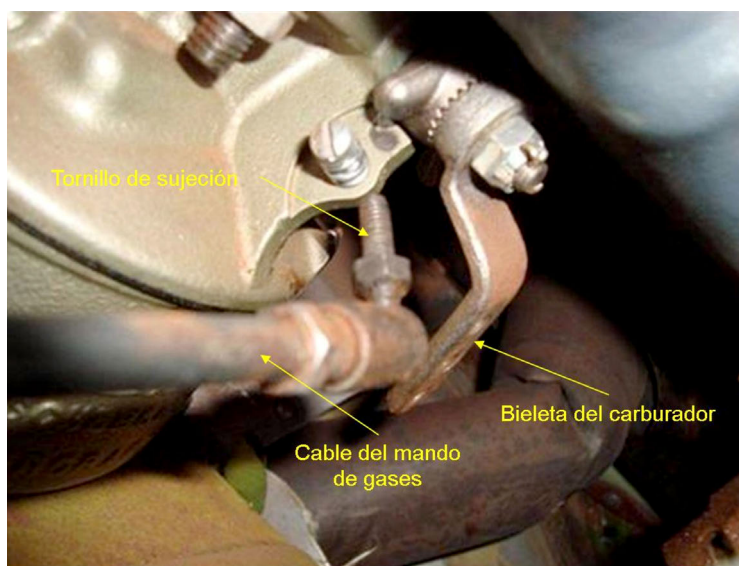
Estado en que se encontró la conexión del cable de gases al carburador
